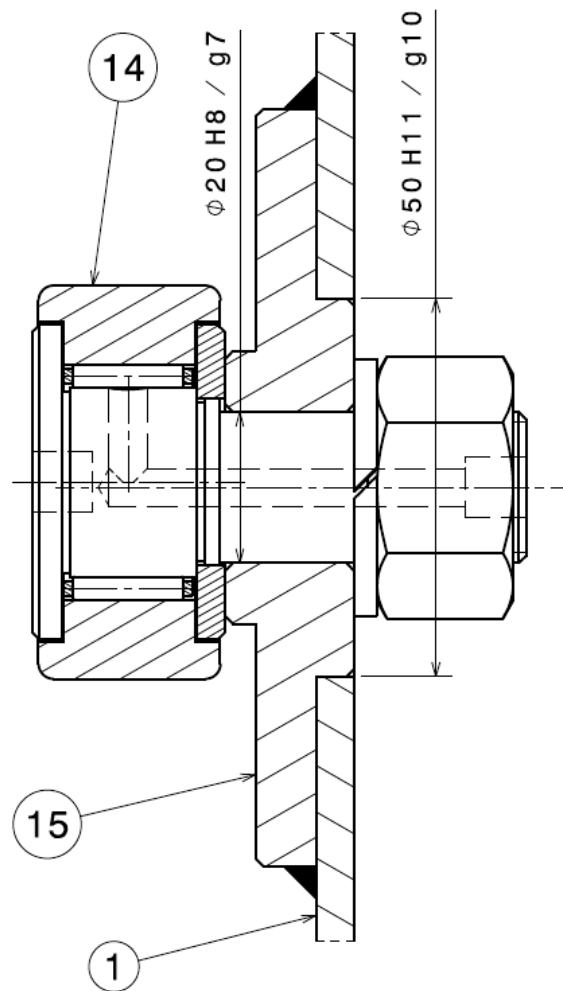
Dessin d'ensemble du montage du galet 14 sur le châssis 1
